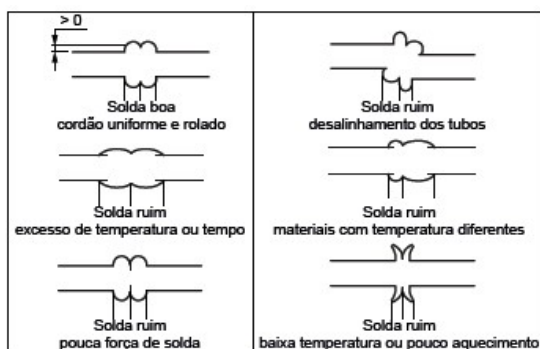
Aspecto típico de uma solda de topo e soldas não conformes
